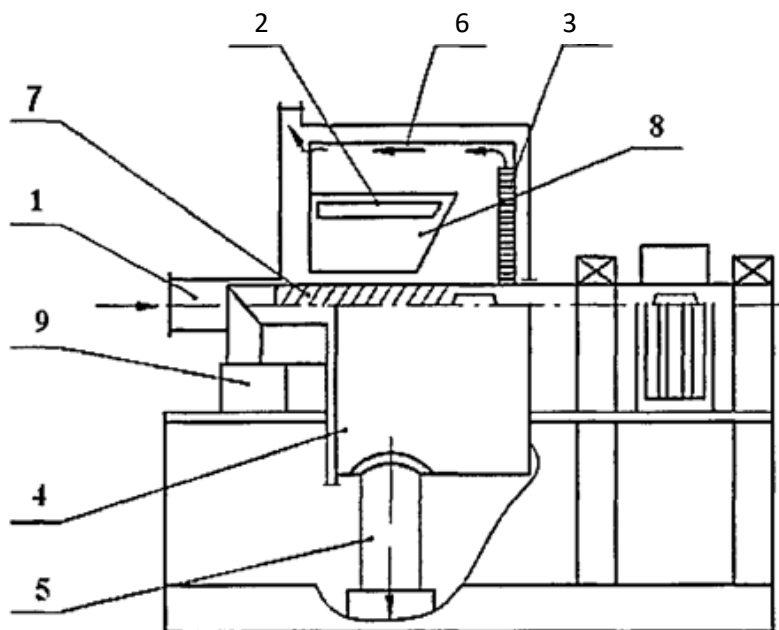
Схема центрифуги с автоматической разгрузкой осадка
